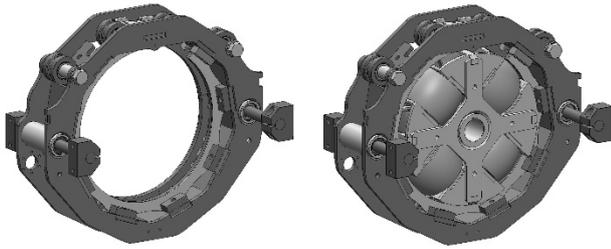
Darstellung der konstruktiven Gestaltung des Führungstunnels (links) sowie Darstellung der gesamten Windebaugruppe (rechts).
